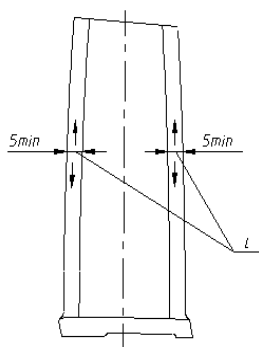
Эскиз рабочей лопаток компрессора с указанием зон упрочнения кромок пера
